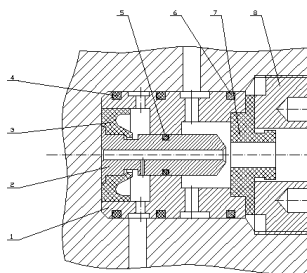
Клапан барабана. 1-корпус клапана; 2-поршень; 3-накладка; 4,6-ущільнюючі кільця; 7-сідло; 8-гайка
